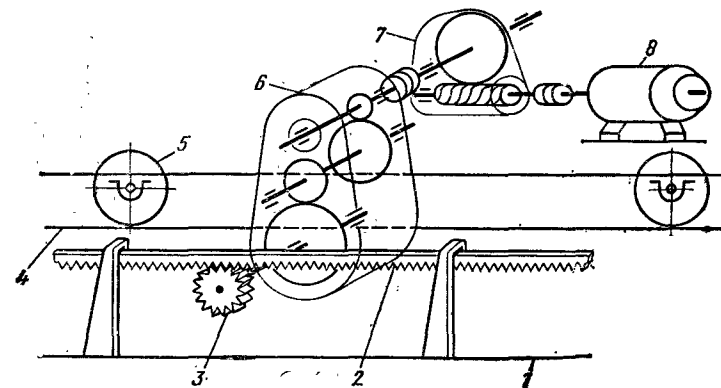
Зубчато-реечный механизм передвижения судового крана козлового:
